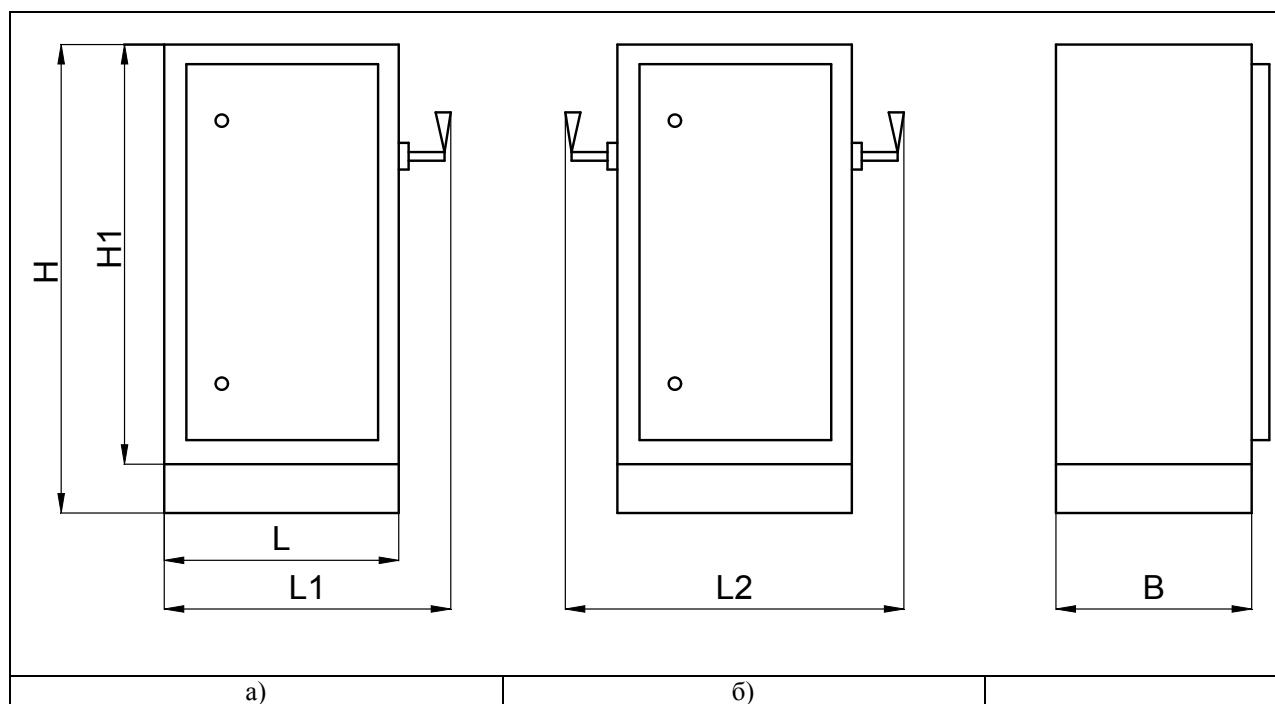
Габаритные и установочные размеры шкафов ШР
